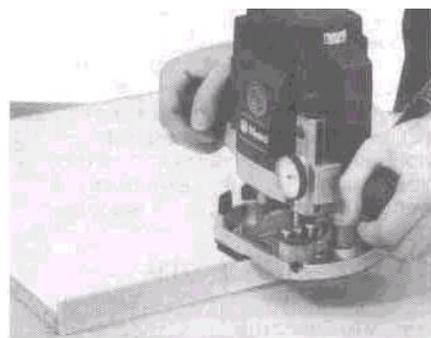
Фрезерование ламината ровно с поверхностью детали. Фрезерная машина с промежуточной платой 31 503.
